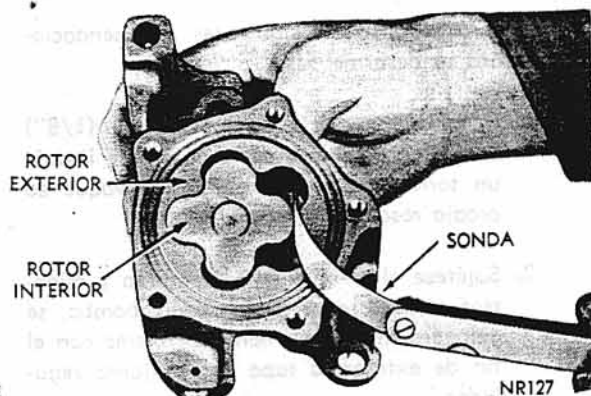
Medición de la tolerancia entre Rotores
